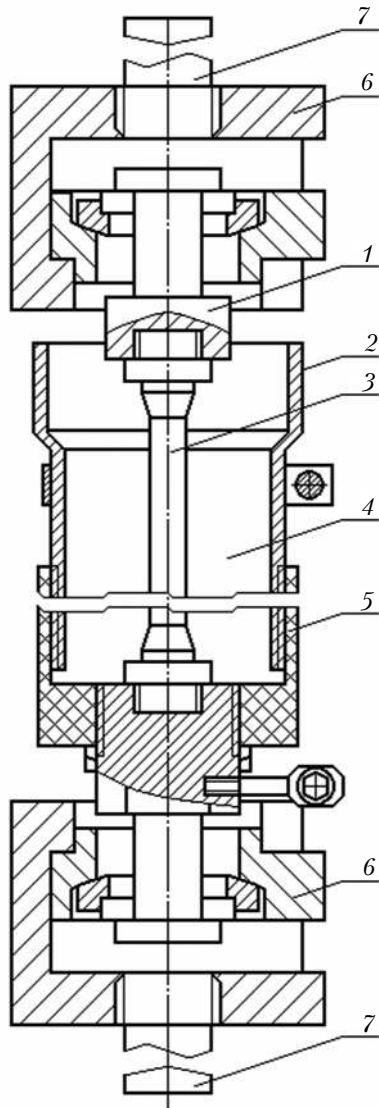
Приспособление для наводороживания образцов в процессе испытаний на растяжение:
